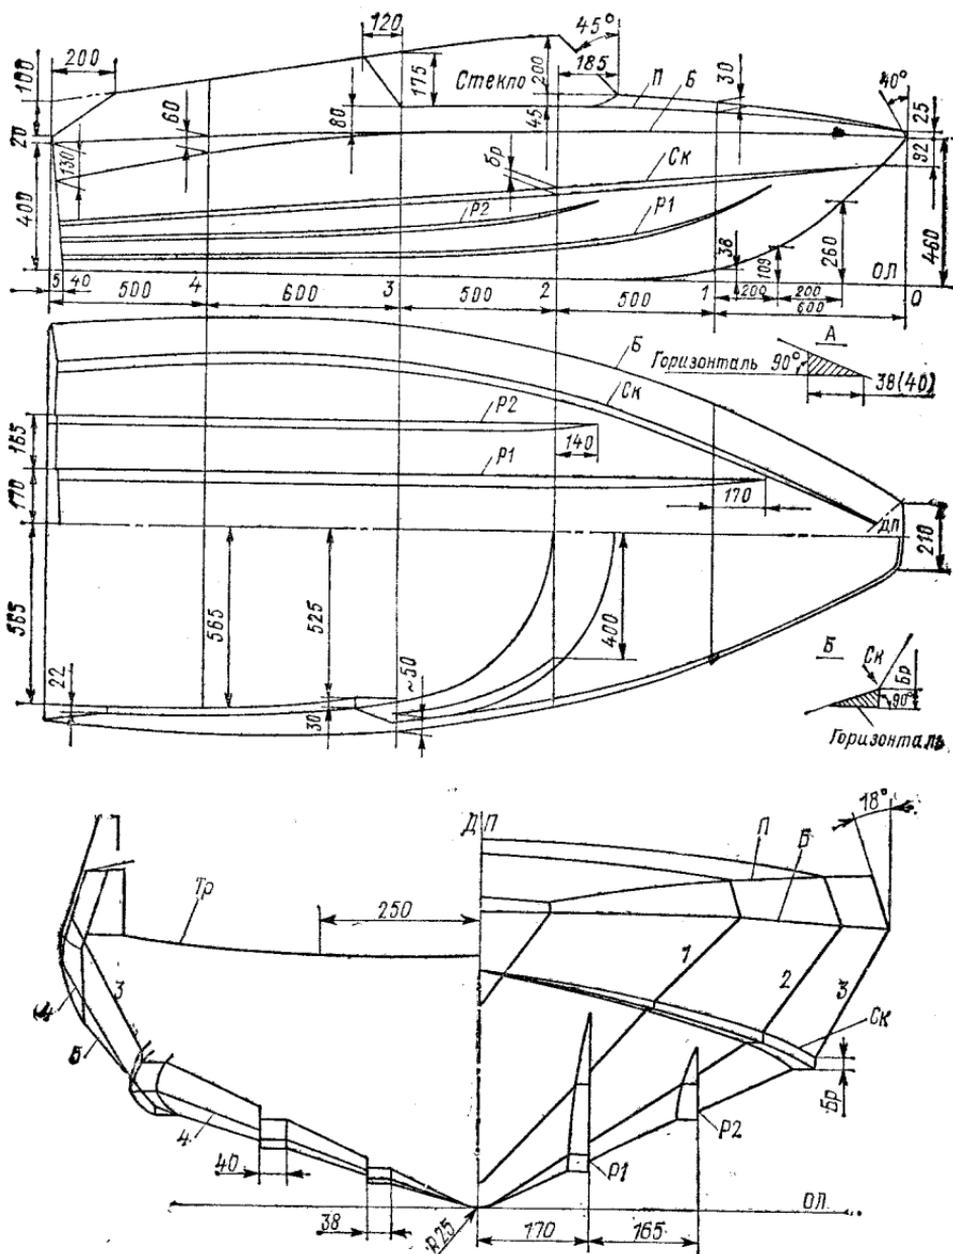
Теоретический чертеж; А — разметка продольного редана; Б — разметка линии скулы и брызгоотбойника.
